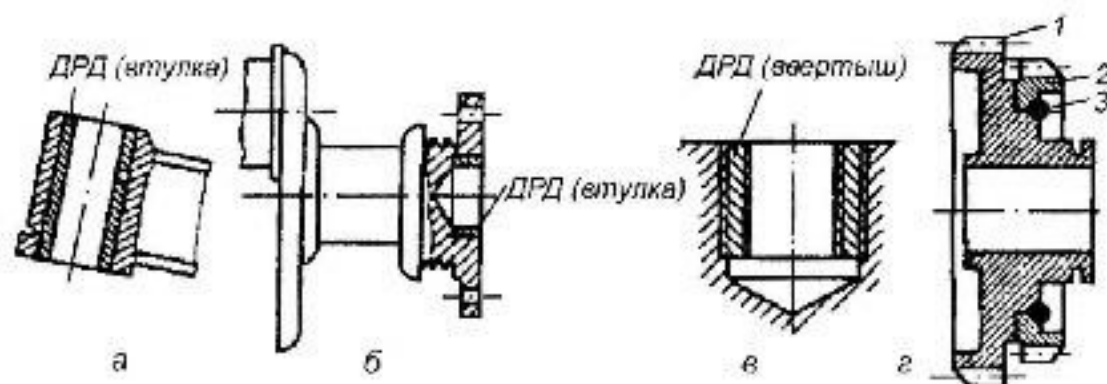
Примеры применения дополнительных ремонтных деталей для восстановления: а, б — цилиндрических отверстий; в — резьбового отверстия; г — венца зубчатого колеса. К расчетной толщине втулки необходимо прибавить припуск на ее механическую обработку после запрессовки.
